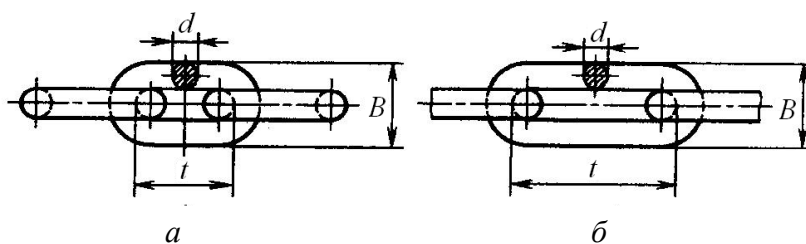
Круглозвенные сварные цепи:
